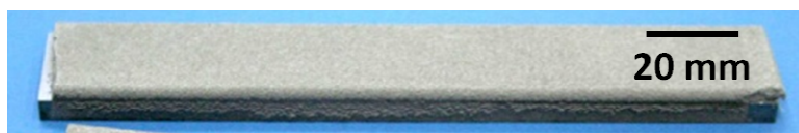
Plaque de revêtement abrasable sur substrat (lot 1)
